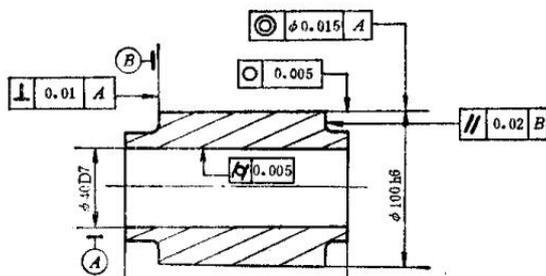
另 (形状公差) 直线度公差应该小于定向公差 (平行度)
